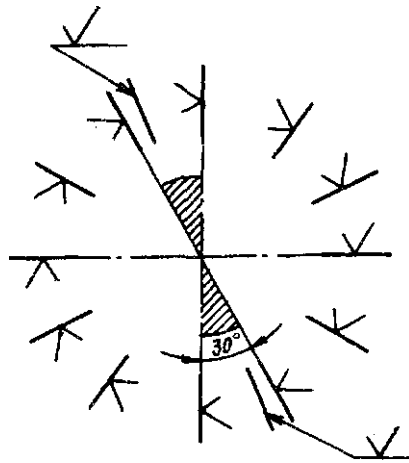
Варианты расположения знака обозначения шероховатости без полки
